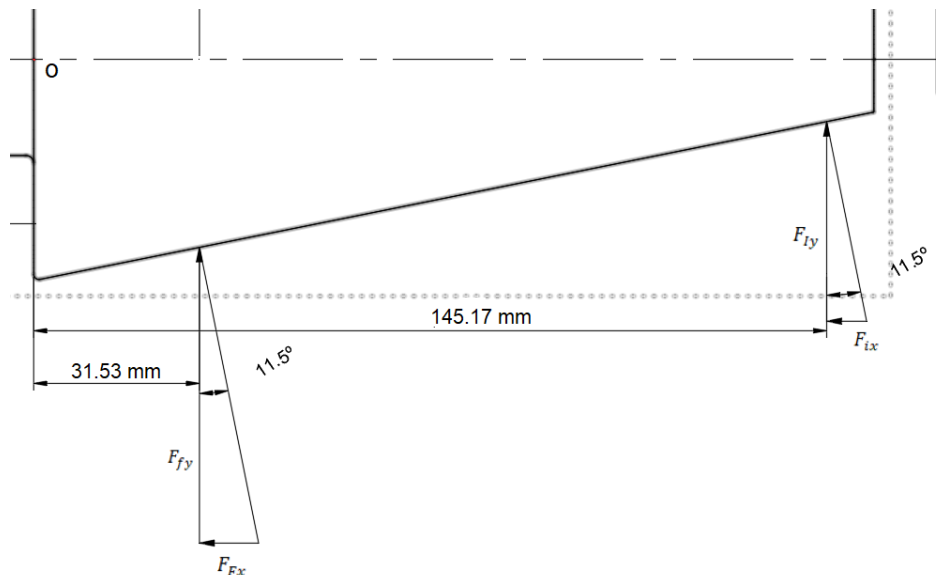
Descomposición de fuerzas rodillo cónico.
